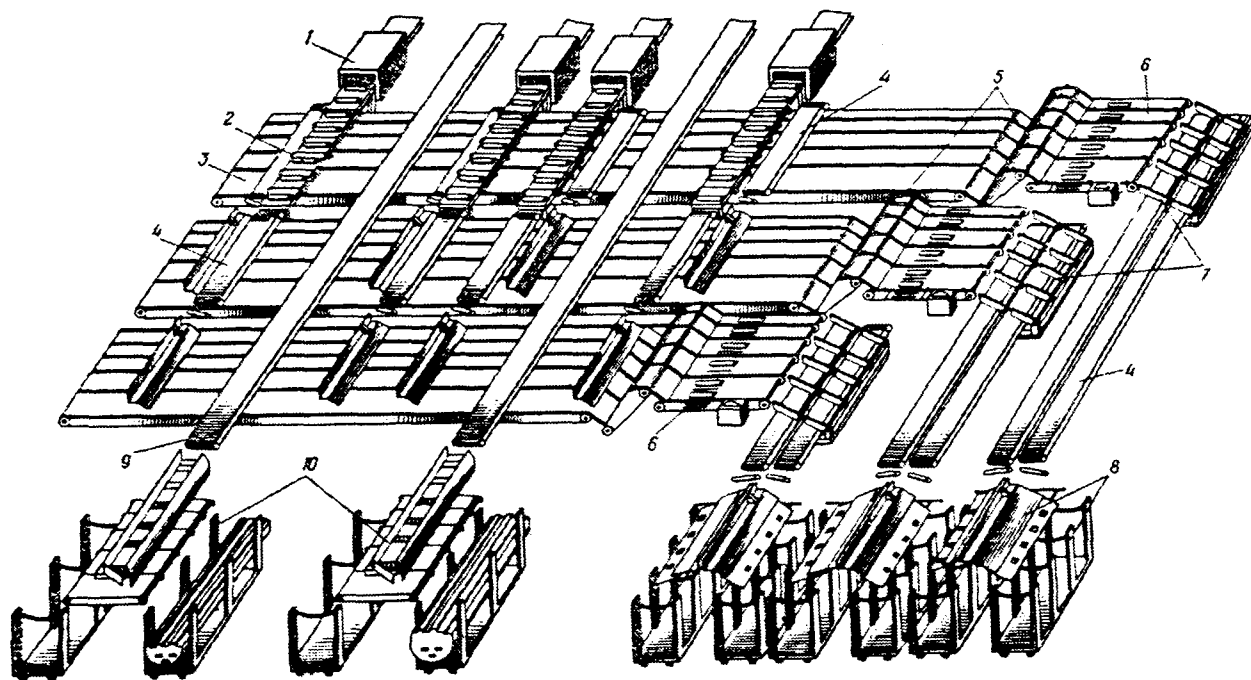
Схема размещения сортировочного оборудования СПР в двухпоточном лесопильном цехе:
